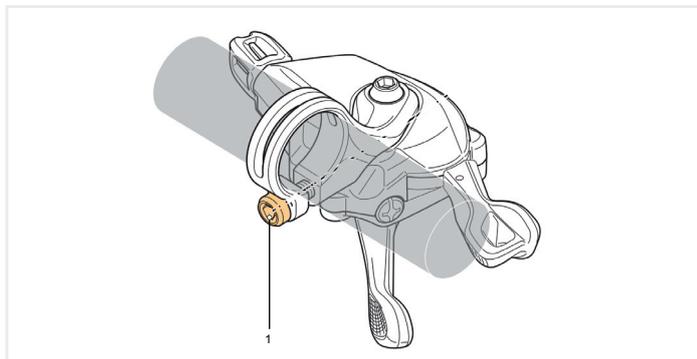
Beispiel Lage Befestigungsschraube (1)
